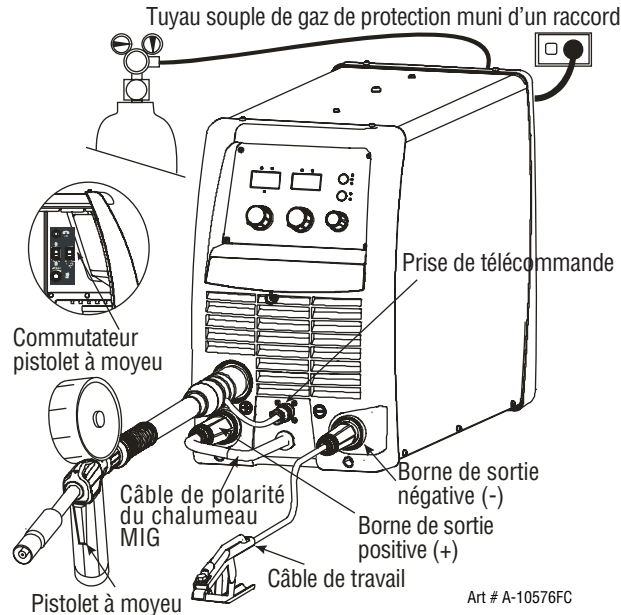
Configuration pour soudage MIG avec fil MIG sous protection gazeuse
